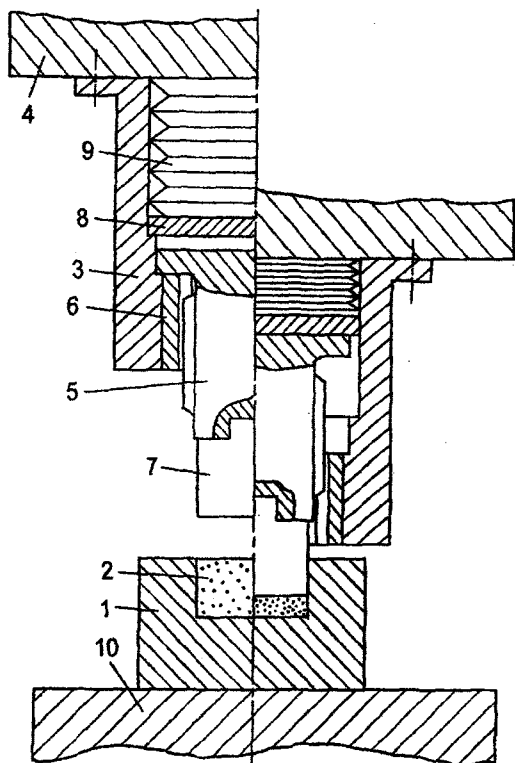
Конструкция штампа для уплотнения заготовки поворачивающимся пуансоном
